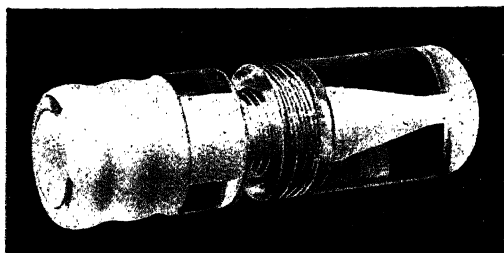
Düsenkörper mit Innen- und Außengewinde (Eingeschnitten mit Widia).
